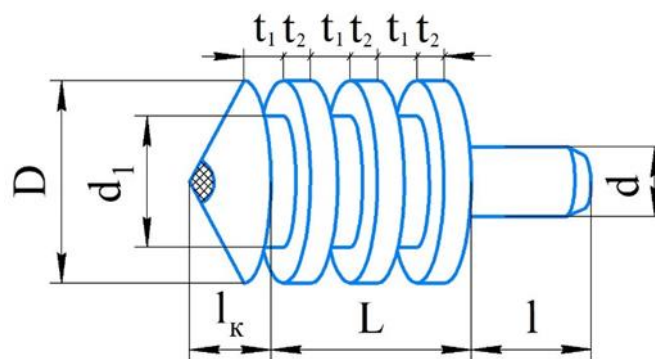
Конструкція індентора з алмазним наконечником у корпусі підвищеної жорсткості: D – зовнішній діаметр корпусу; d_1 – внутрішній діаметр у зоні конічної частини; d – діаметр хвостової частини; L – довжина корпусу; l – довжина монтажної ділянки; l_k – довжина конічної частини; t , t_1 , t_2 – параметри кільцевих жорсткісних виступів [56].
